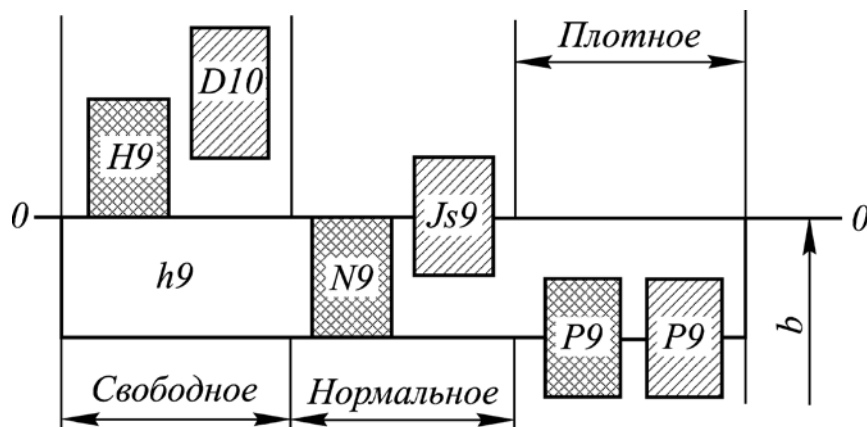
Поля допусков для шпоночных соединений:
